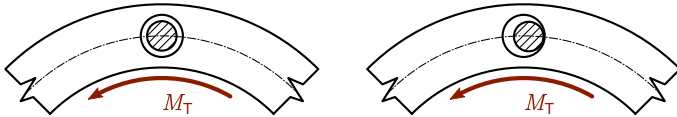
Einseitige Anlage der Schraube am Freilaufaußenring unter Drehmomentbelastung
